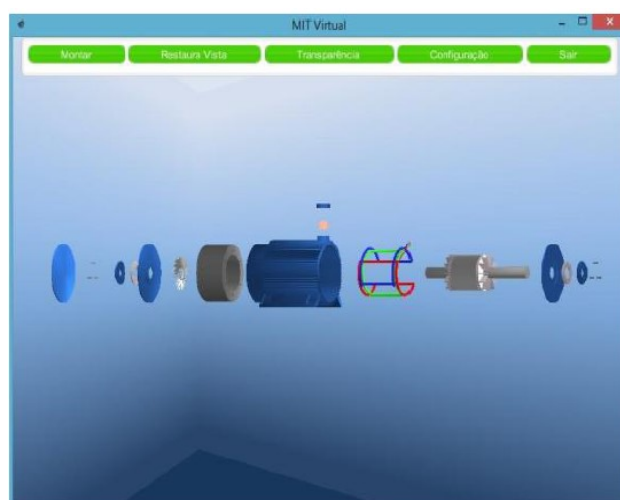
Interface do Módulo de Apoio didático com a vista explodida do motor.
